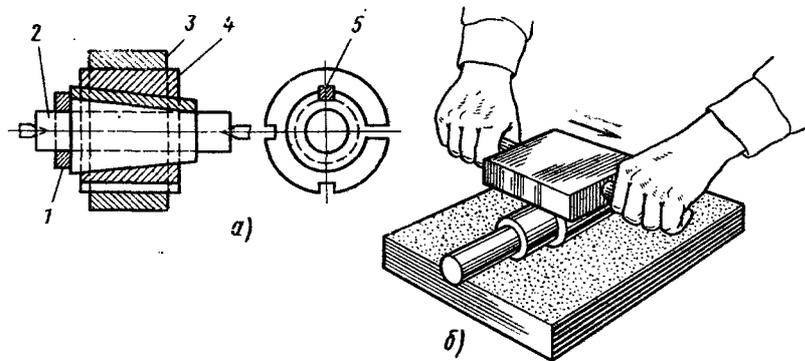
Подготовка к притирке внутренней цилиндрической поверхности втулки: а — устройство притира; 1 — гайка; 2 — оправка; 3 — втулка; 4 — притир; 5 — шпонка; б — прием шаржирования цилиндрического притира на плите
